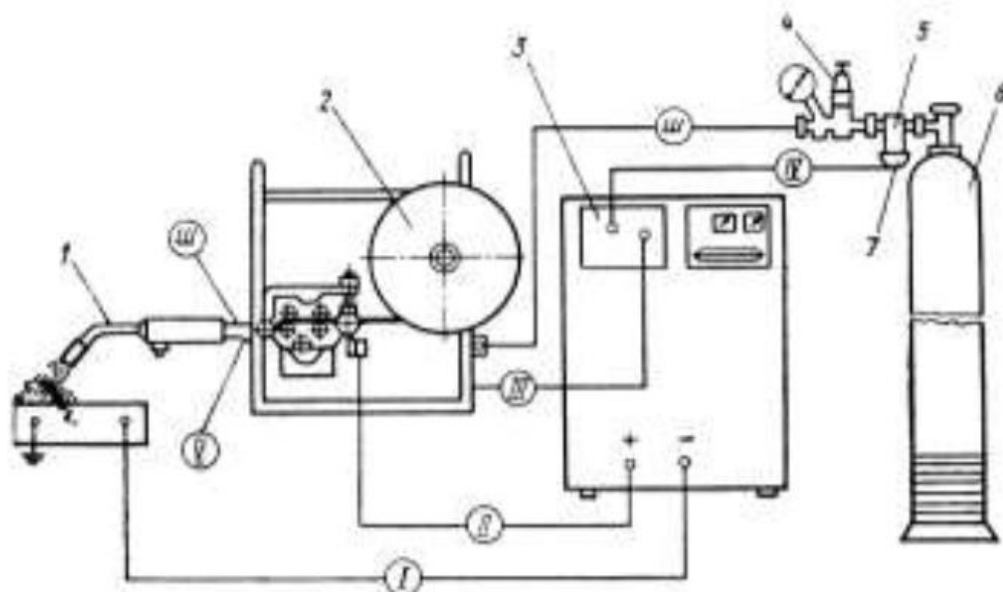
Схема установки для напівавтоматичного зварювання і наплавлення в середовищі вуглекислого газу: 1 – палик зварювальний; 2 – механізм подаючий; 3 – джерело живлення; 4 – редуктор; 5 – осушувач; 6 – балон з вуглекислим газом; 7 – підігрівач; I-IV – з'єднувальні кабелі; Ш – шланги
